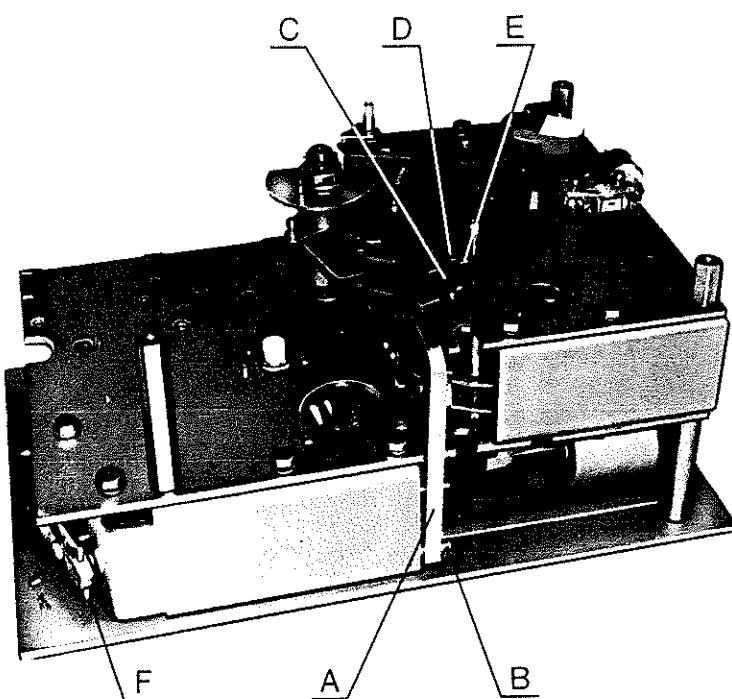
Montaggio dispositivo di scarica dell'energia
